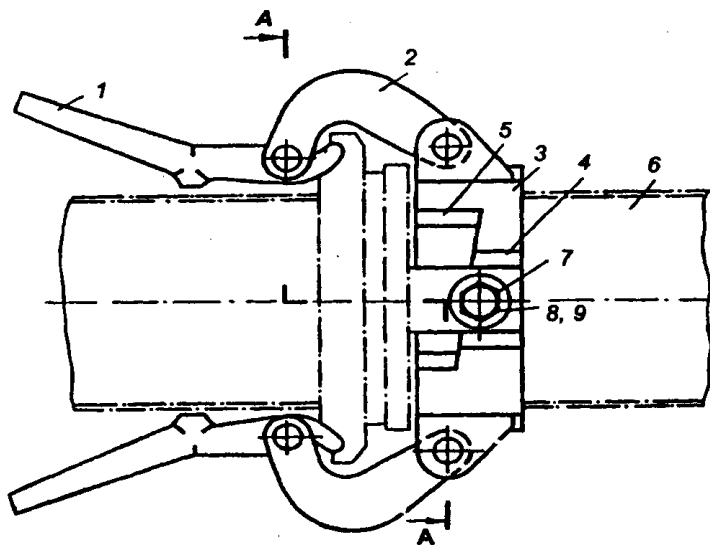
Двухрычажный быстроразъёмный замок: 1 –
